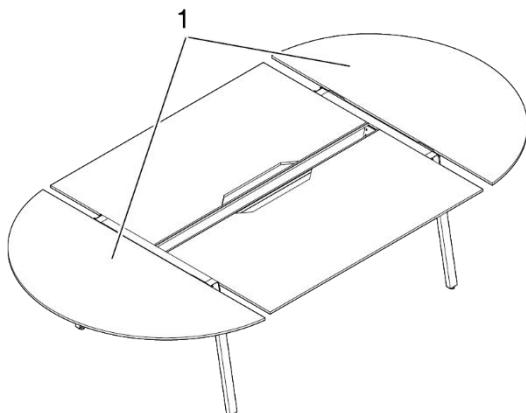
Halbrunde Anbauplatte, zulässiger Anbau
